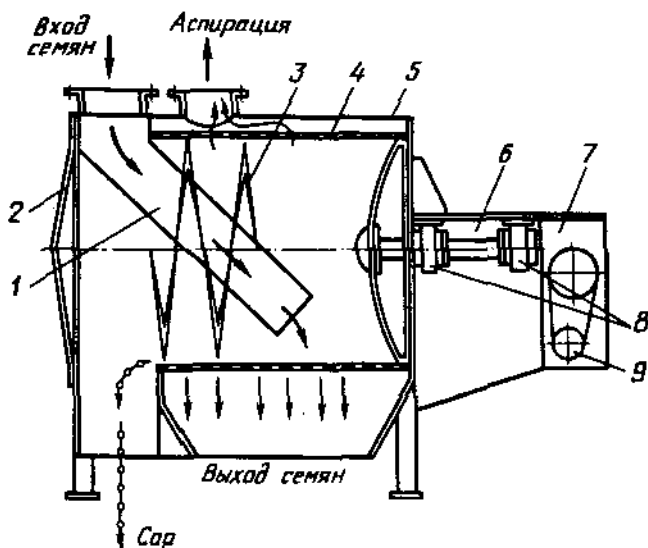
Барабанный сепаратор А1-БЗО (скальператор)
